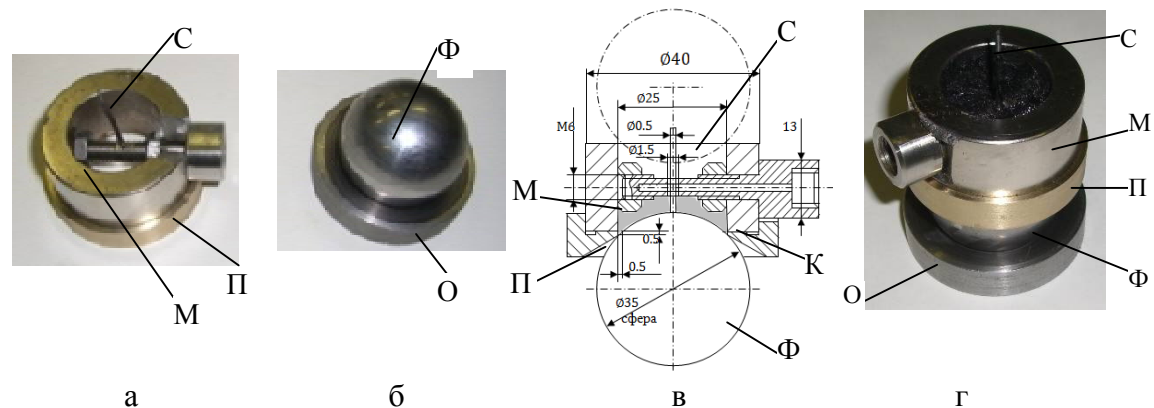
Технологічні операції з формування першої сферичної поверхні шарніра: а – встановлення проставки П на корпус шарніра та стрижня С в отвір патрубка; б – точна куля, по якій формується сферична поверхня I; в – геометричні розміри, що визначають розташування шарніра і кулі; г – нанесення металополімера в отвір магніта, який встановлено на кулі
